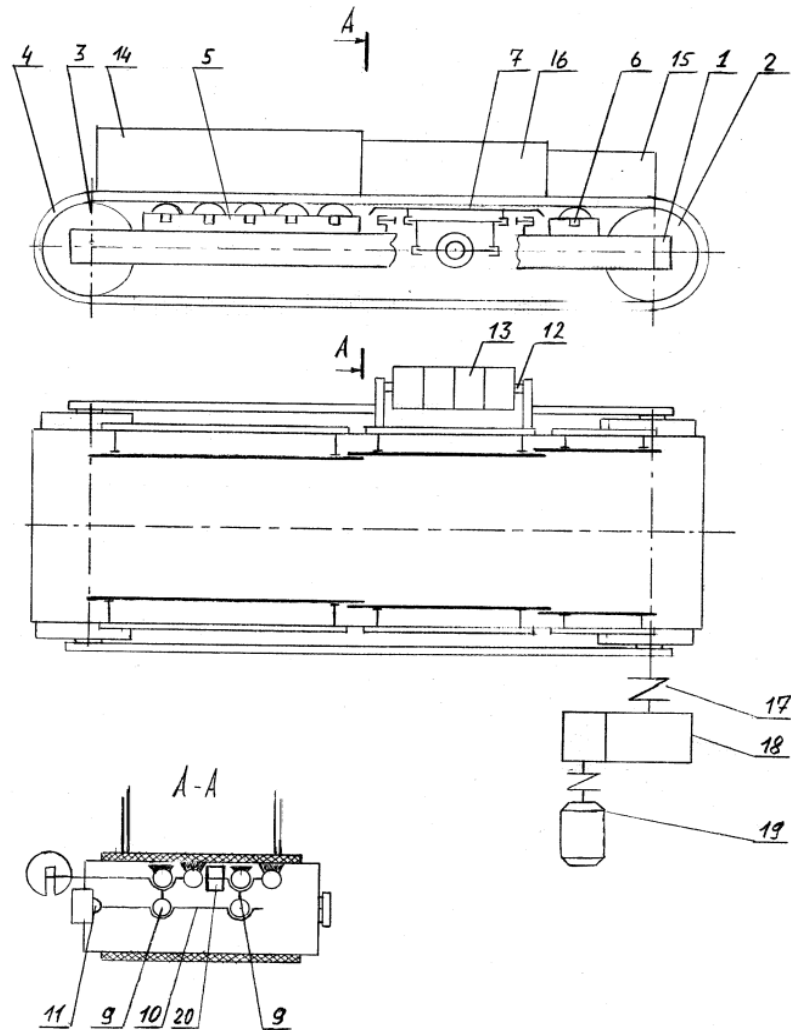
Устройство и внешний вид ленточного весодозатора
